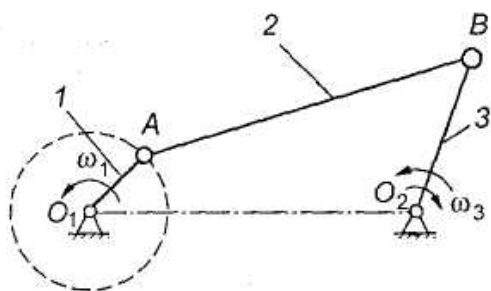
Шарнирный четырёхзвенный механизм: 1 – кривошип; 2 – шатун; 3 – коромысло
